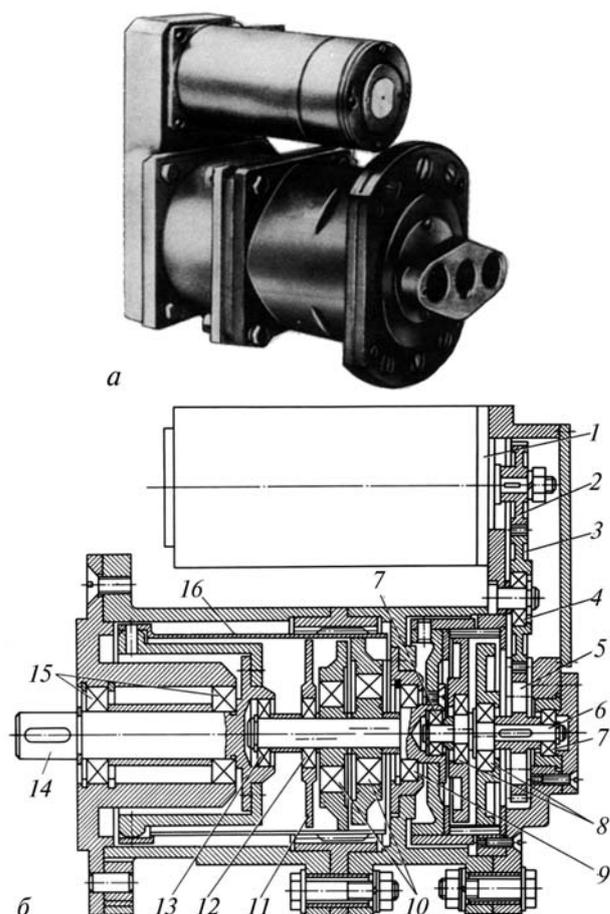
Силовой привод с двухступенчатой волновой передачей:
